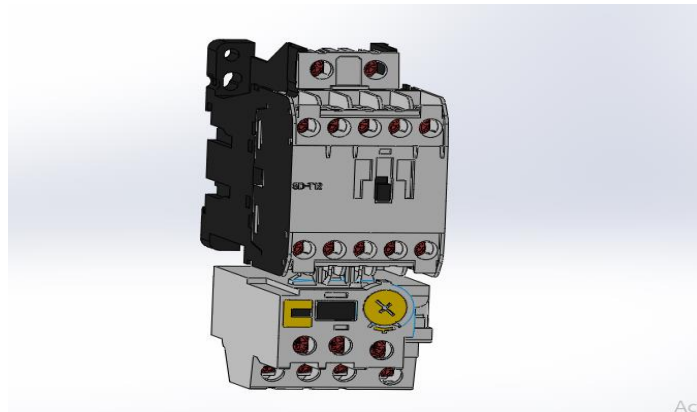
Dessin de contacteur et relais thermique en 3D avec SOLIDWORKS
